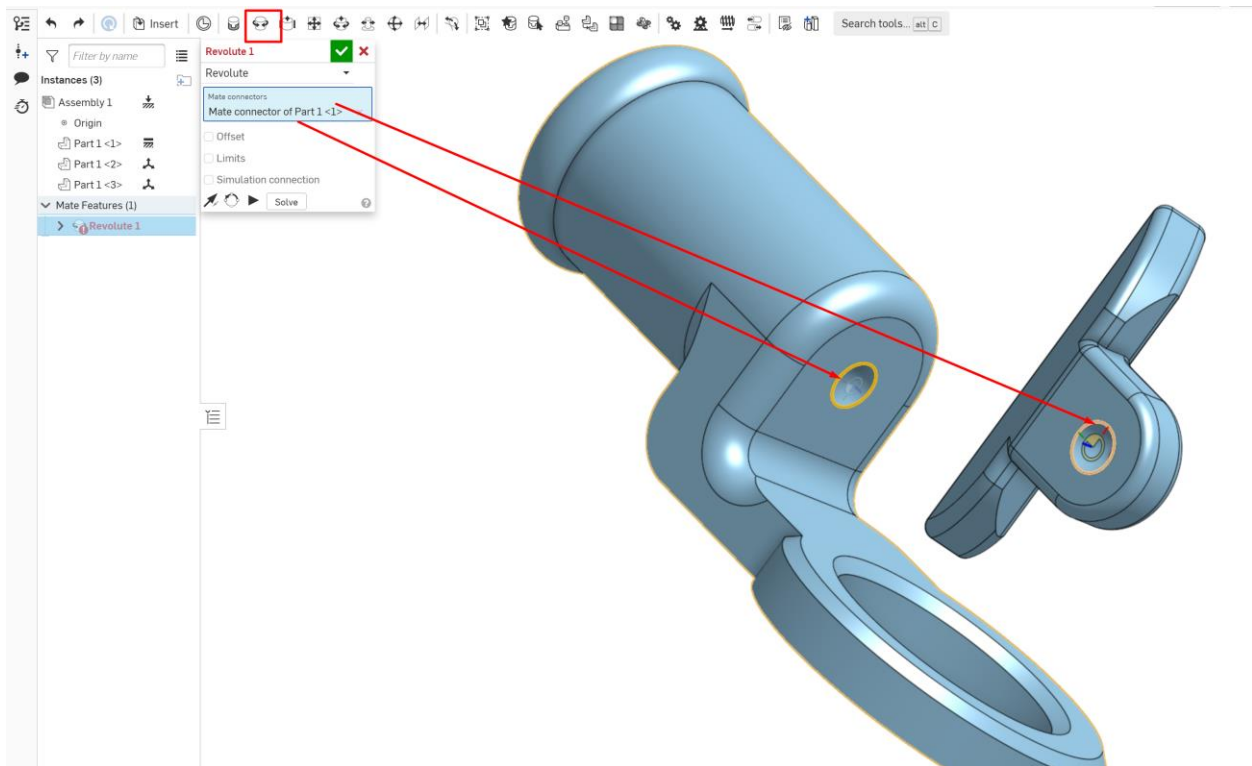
Складання поворотної рукоятки (використання сполучень деталей)
